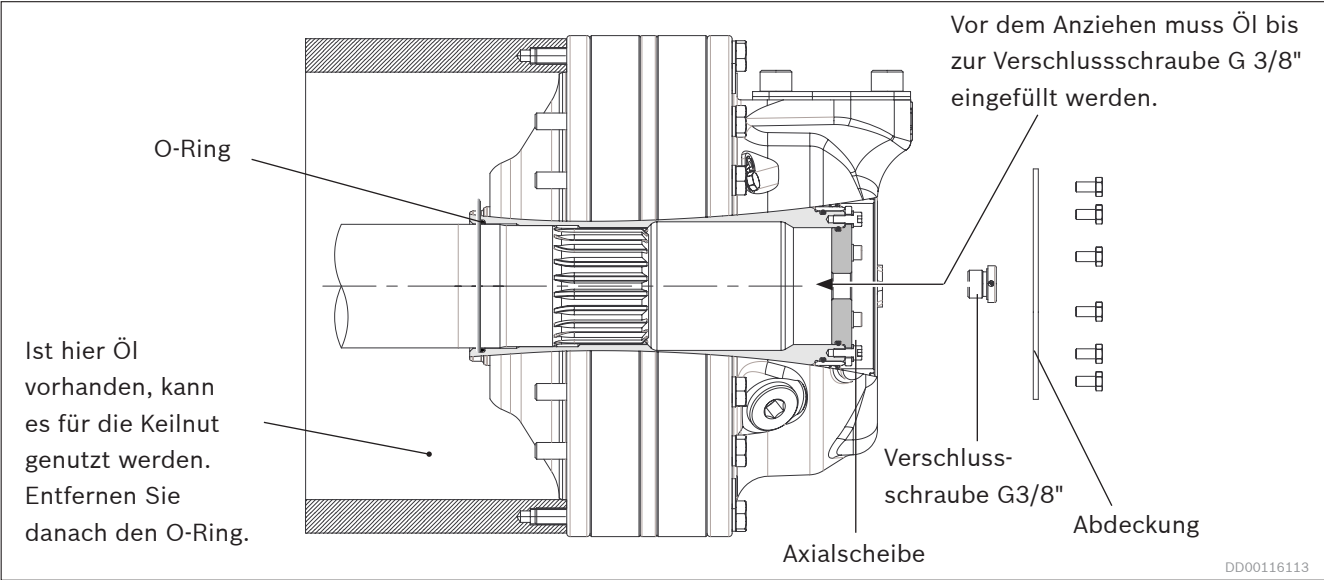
Beispiel Motor mit Flanschmontage, waagrechte Welle
